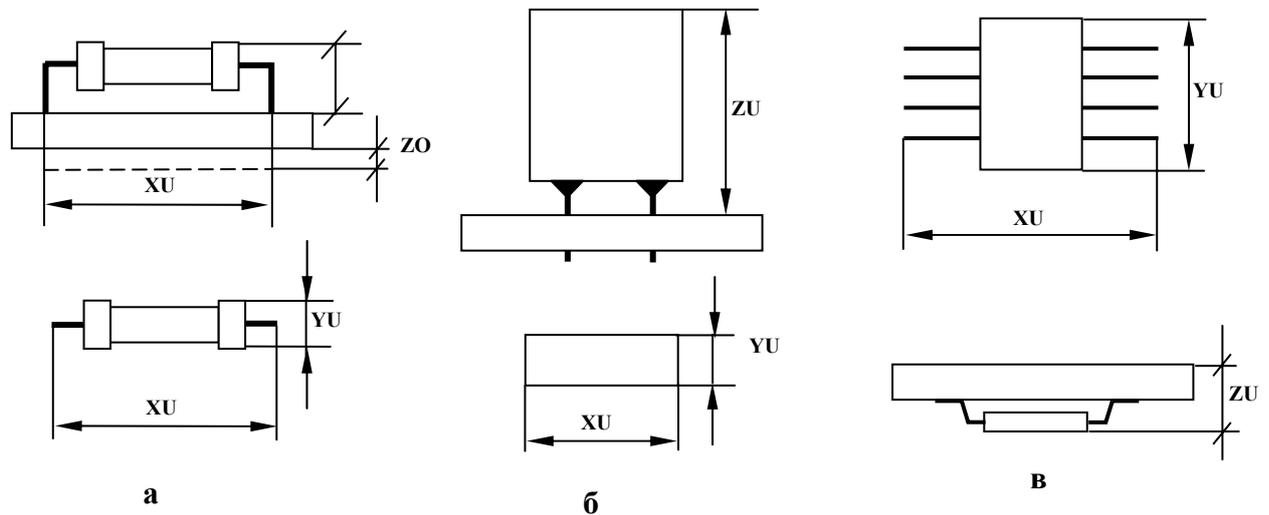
Установочные размеры элементов на печатной плате: а – резисторы; б – конденсаторы КМ 6; в – микросхемы в корпусах 401, 402.
